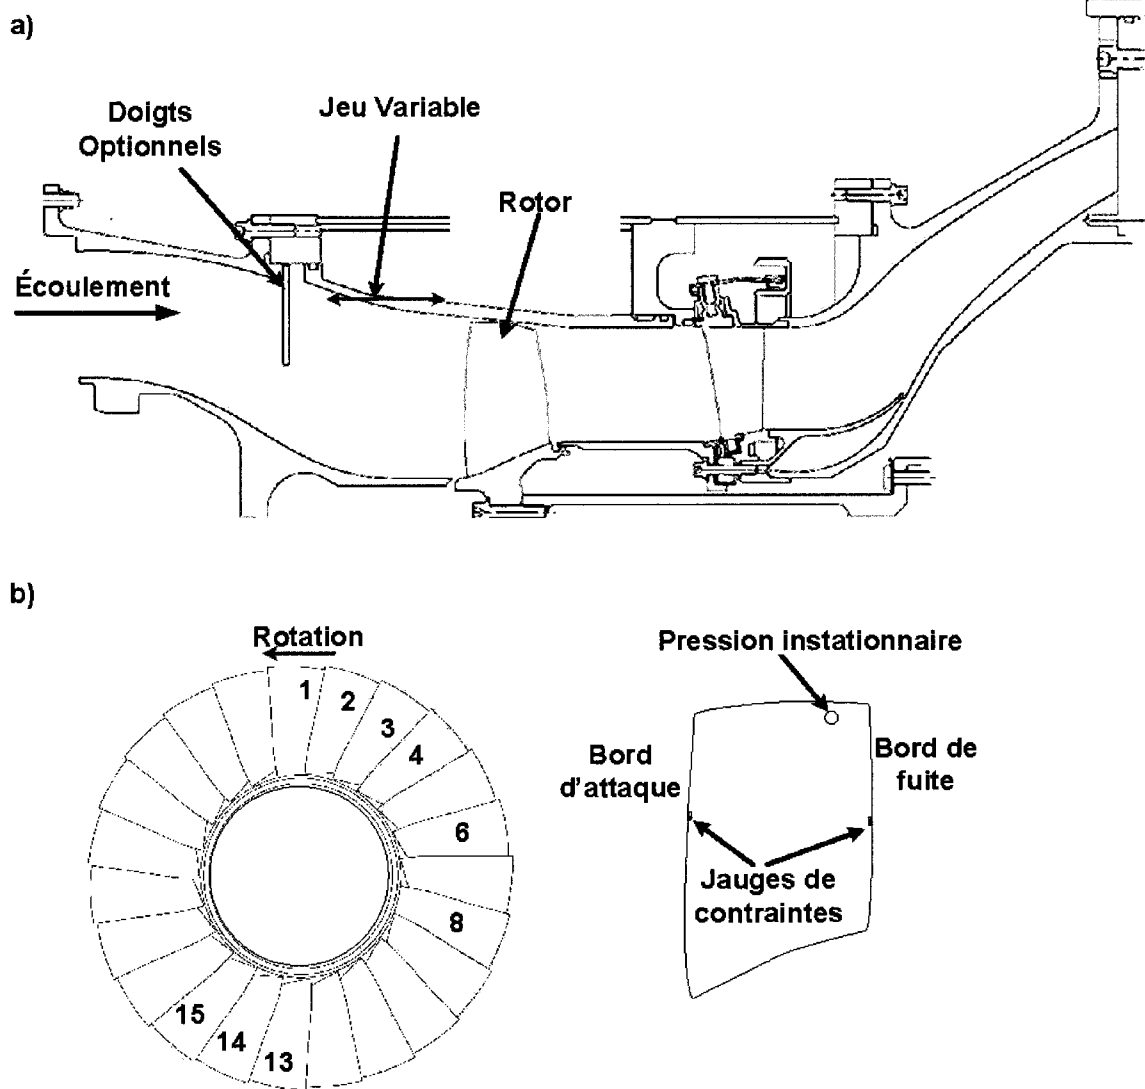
6. a) Coupe méridionale de la section d'essai b) Instrumentation rotative
